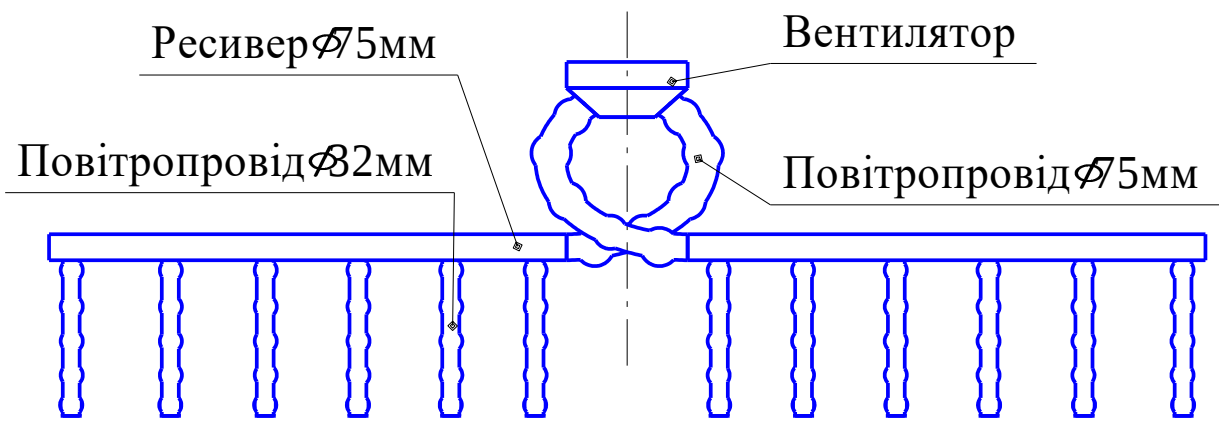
Схема формування повітропроводів вздовж конструкції сівалки.
